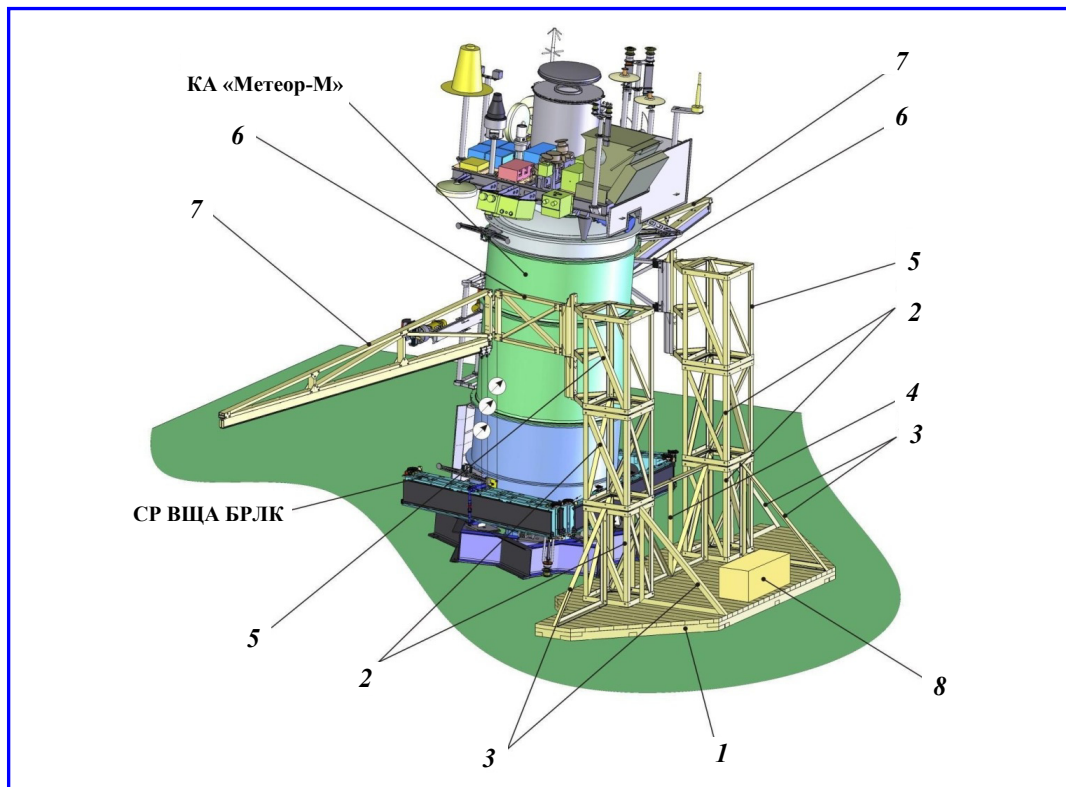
КА на стенде раскрытия: 1 – основание; 2, 5 – фермы; 3 – раскосы; 4 – перемычка; 6 – поворотные рамы; 7 – стрелы; 8 – груз-противовес
